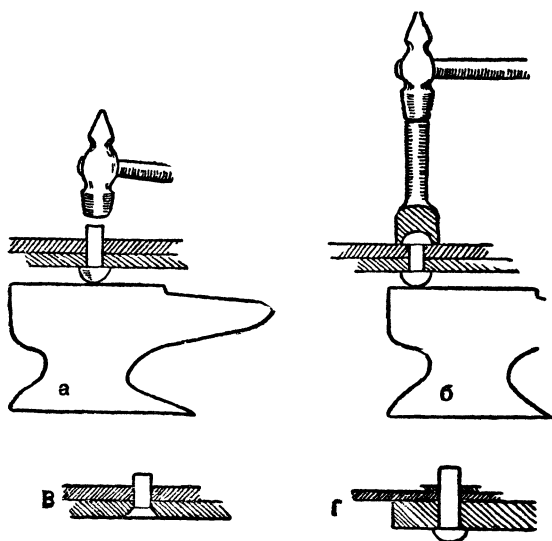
Соединение металла заклепками: а — расклепывание головки, б — формовка головки, в — заклепки с потайной головкой, г — заклепка с шайбой.
